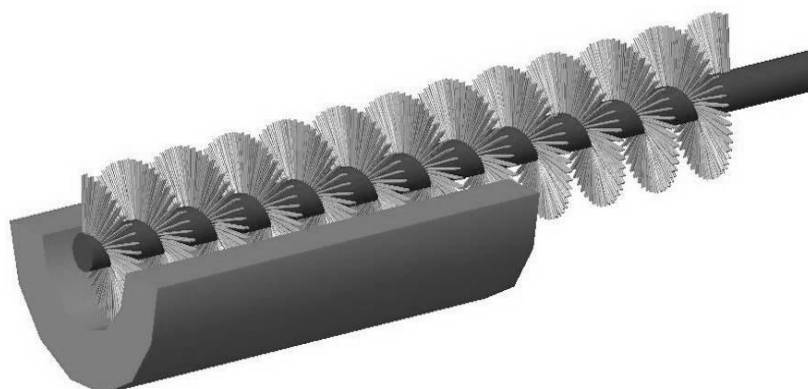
Спрощена модель схеми обробки заготовки гвинтовим ЕПАІ
